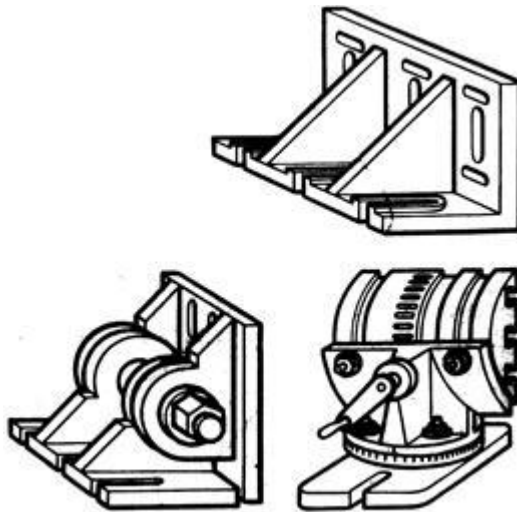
Кутові плити для закріплення заготовок на столі фрезерного верстата
